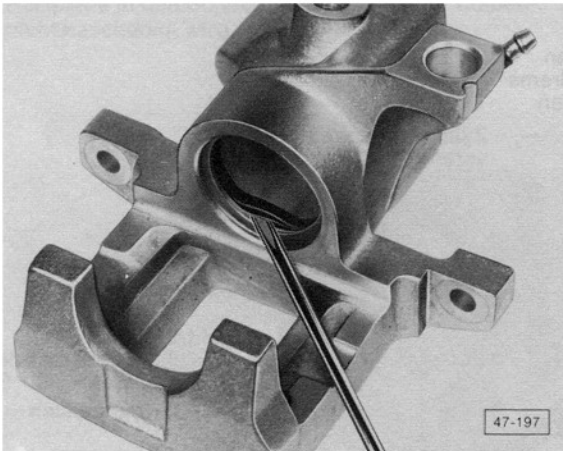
Dichtring vorsichtig mit einem Schraubenzieher herausnehmen
